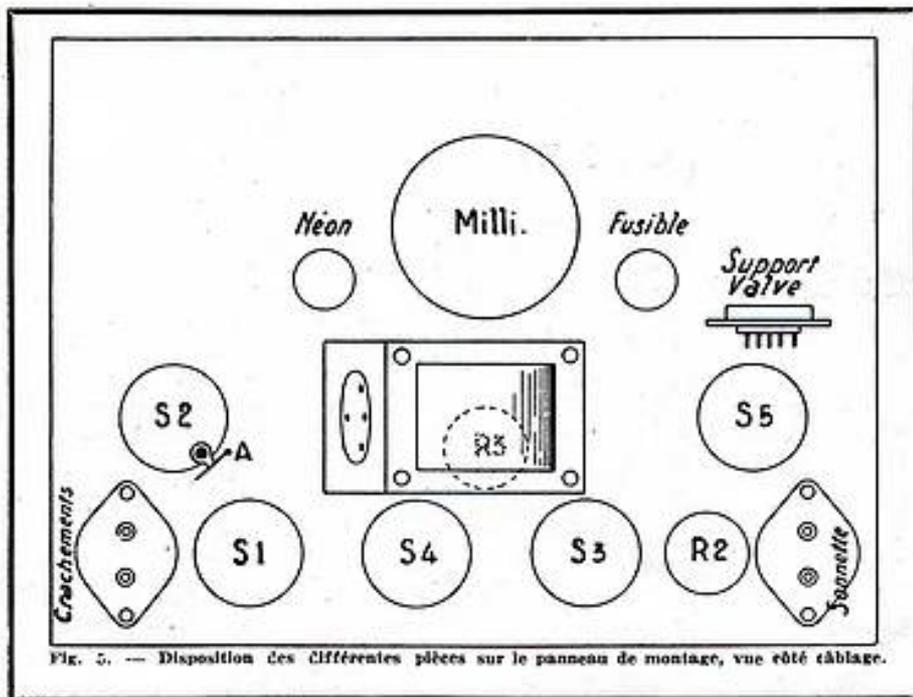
Disposition des différentes pièces sur le panneau de montage, vue côté câblage.
